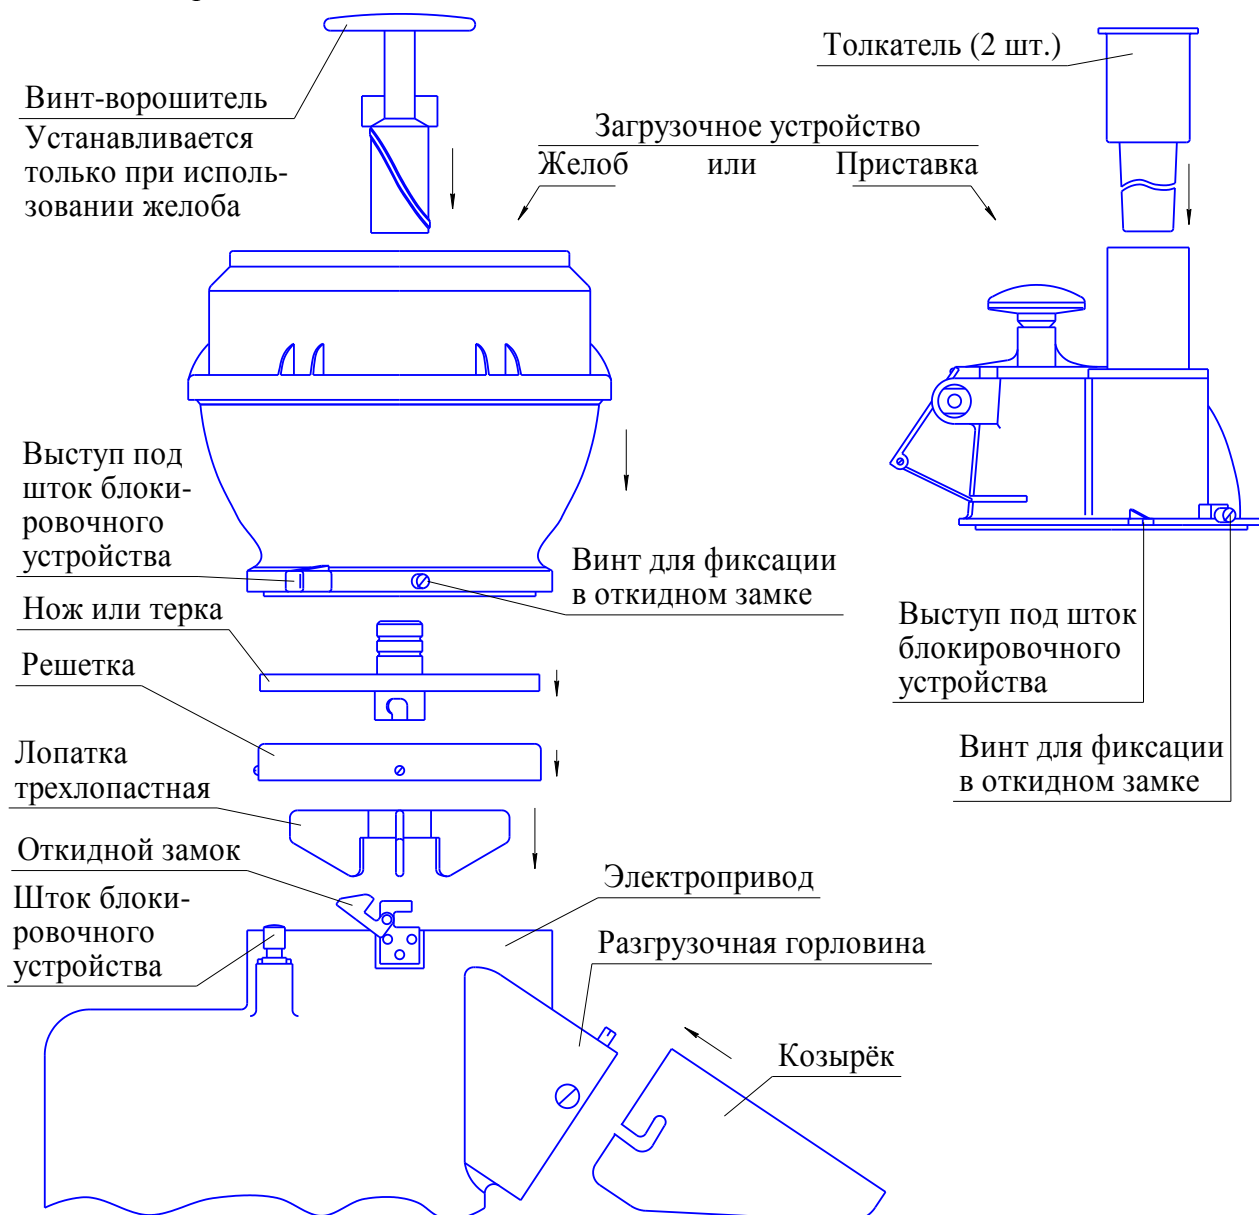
Порядок сборки машины для переработки овощей, фруктов и сыров
